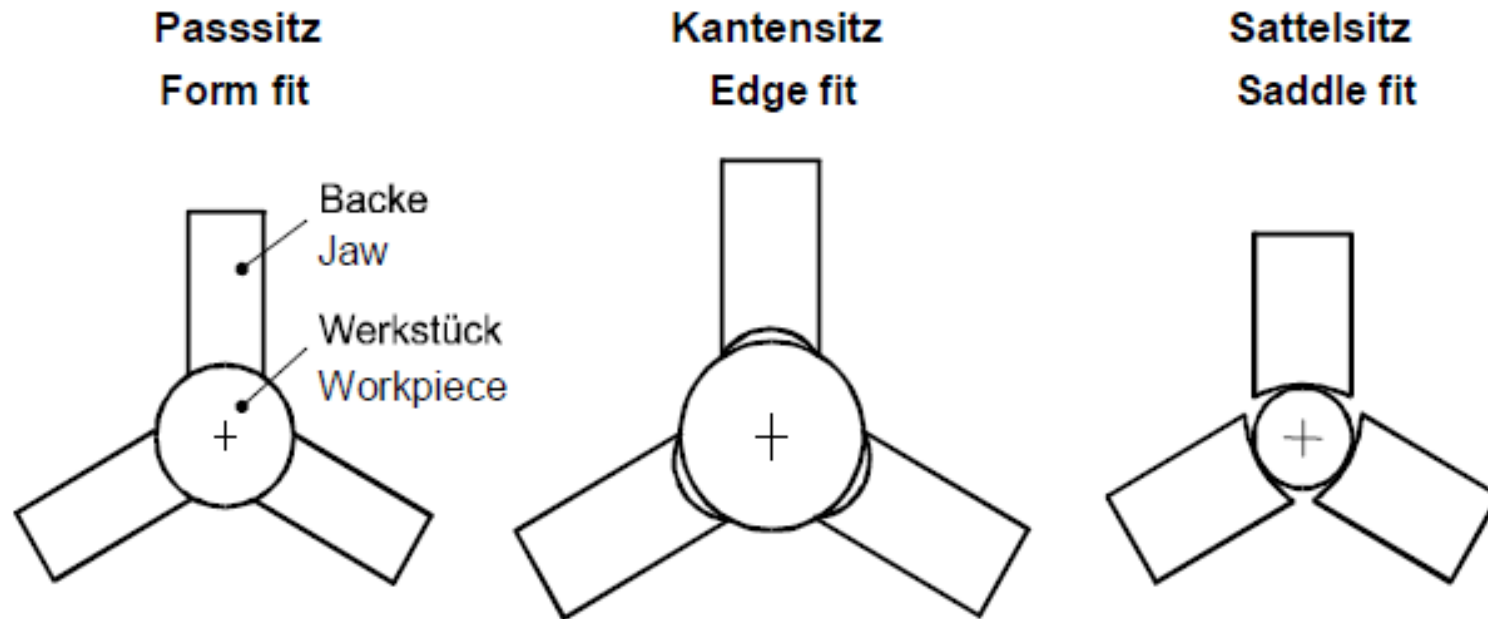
Berührungsformen zwischen glatten Aufsatzbacken und Werkstück
